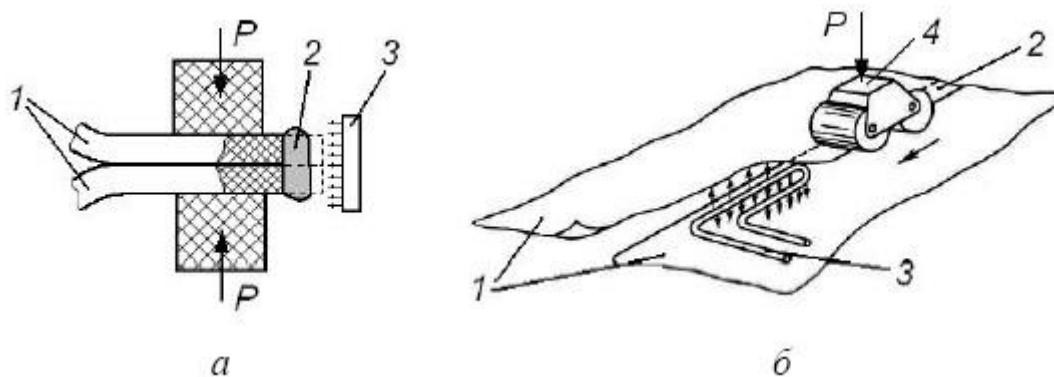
Схема сварки ИК-излучением рантового шва (а) соединения внахлестку (б) 1 - свариваемые пленки; 2 - сварной шов; 3 - ИК - излучатель; 4 - прикатывающие ролики
